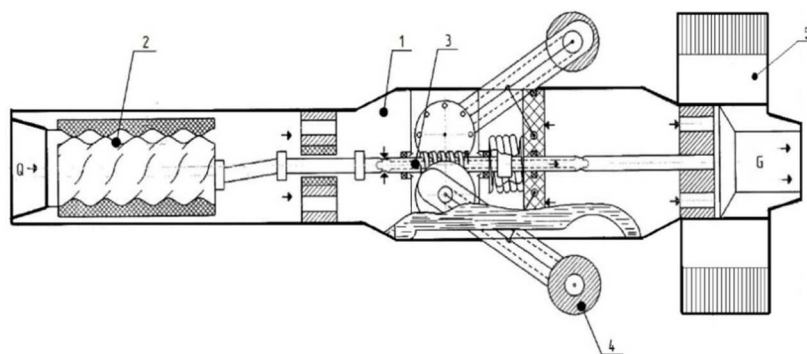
Внутритрубный гидромеханический трактор: 1 – цилиндрический корпус; 2 – героторная пара; 3 – зубчатый червячно-цевочный механизм; 4 – рабочее колесо; 5 – насадка-скребок
